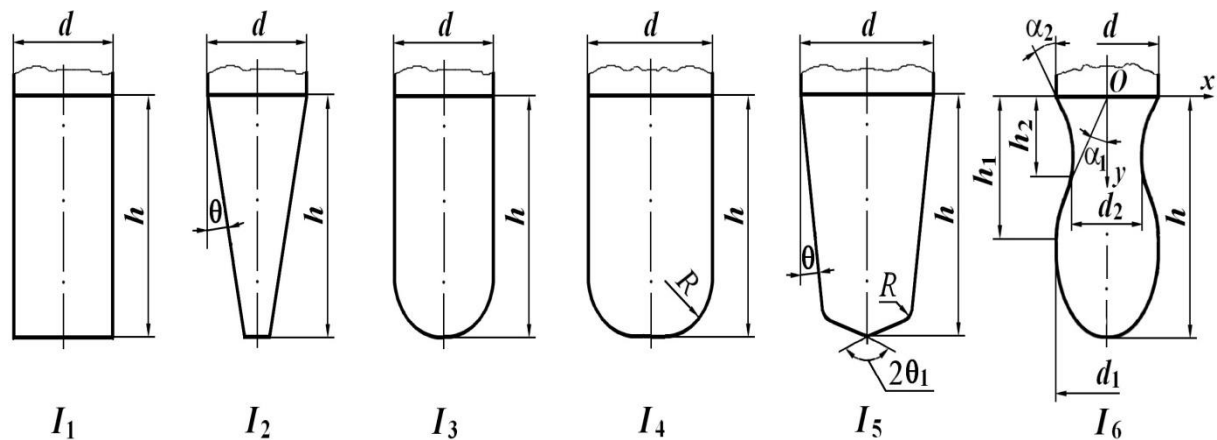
Різальний інструмент для оброблення складних поверхонь деталей на багатокоординатних станках із числовим програмним керуванням:
